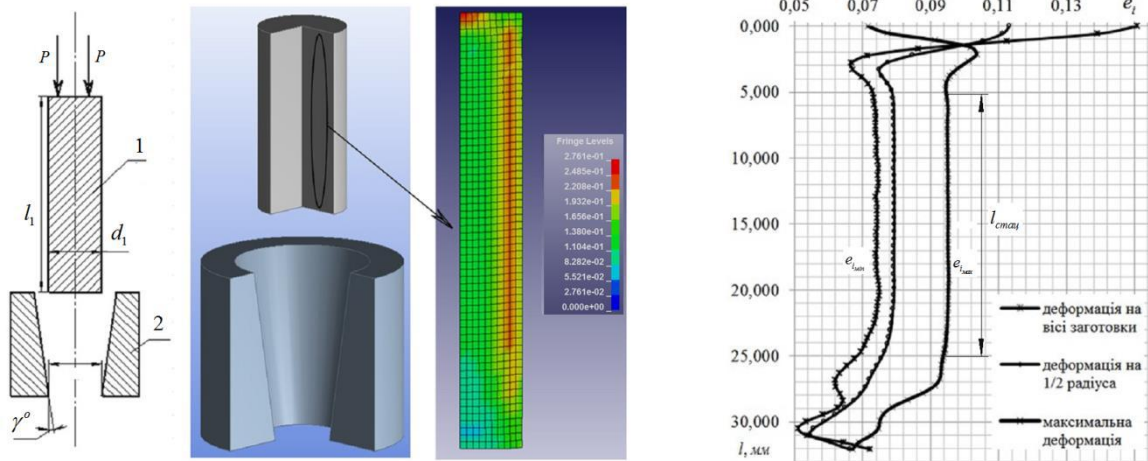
Редукування заготовки (1 – заготовка, 2 – матриця)
